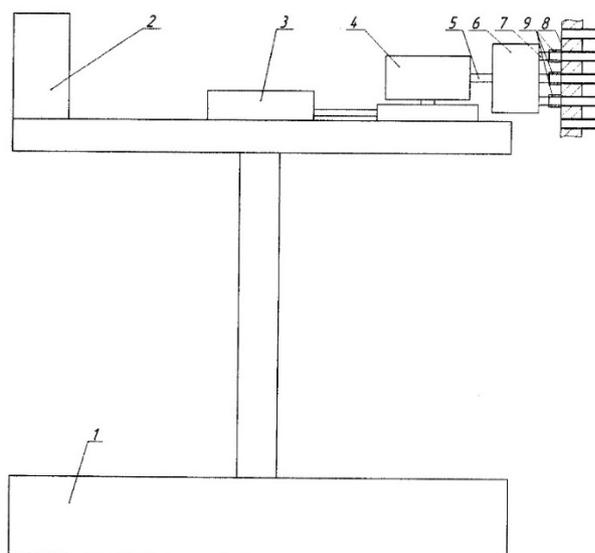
Устройство для сварки трением комбинированных соединений трубы с трубной решеткой теплообменных аппаратов
